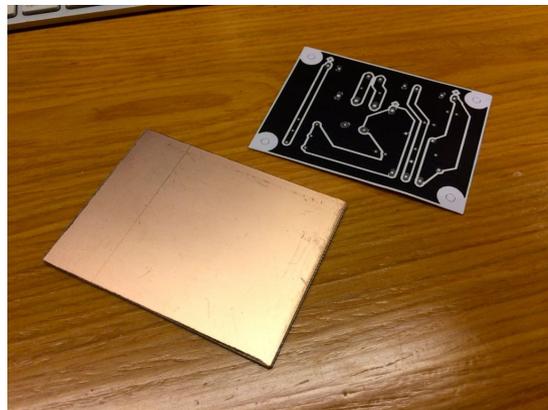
Placa de circuito impresso virgem com o diagrama da placa a ser montada.
